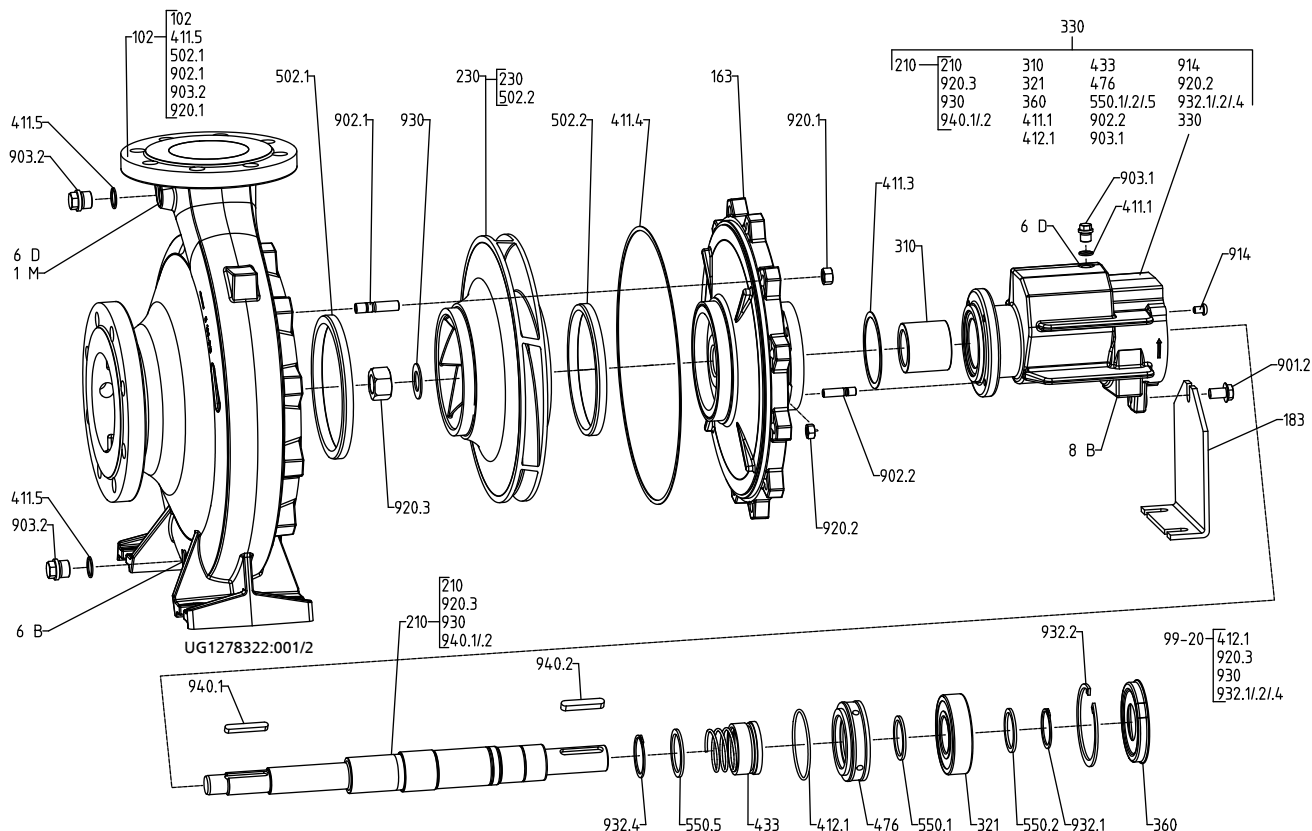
Деталировочный чертеж Etanorm SYT, WE 35
